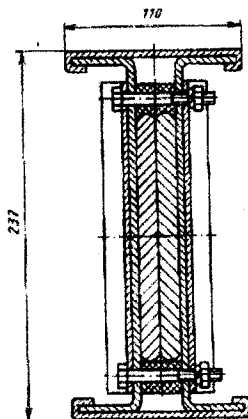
Поперечний переріз магістральних шинопроводів ШМАД-1600-44-1УЗ і ШМАД-2500-44-1УЗ
